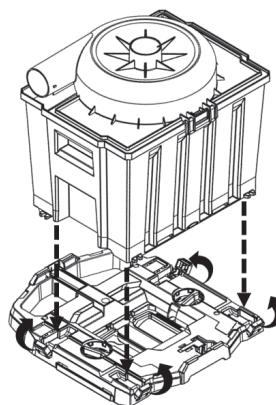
Pré-separador sobre a placa de adaptador Unifix
